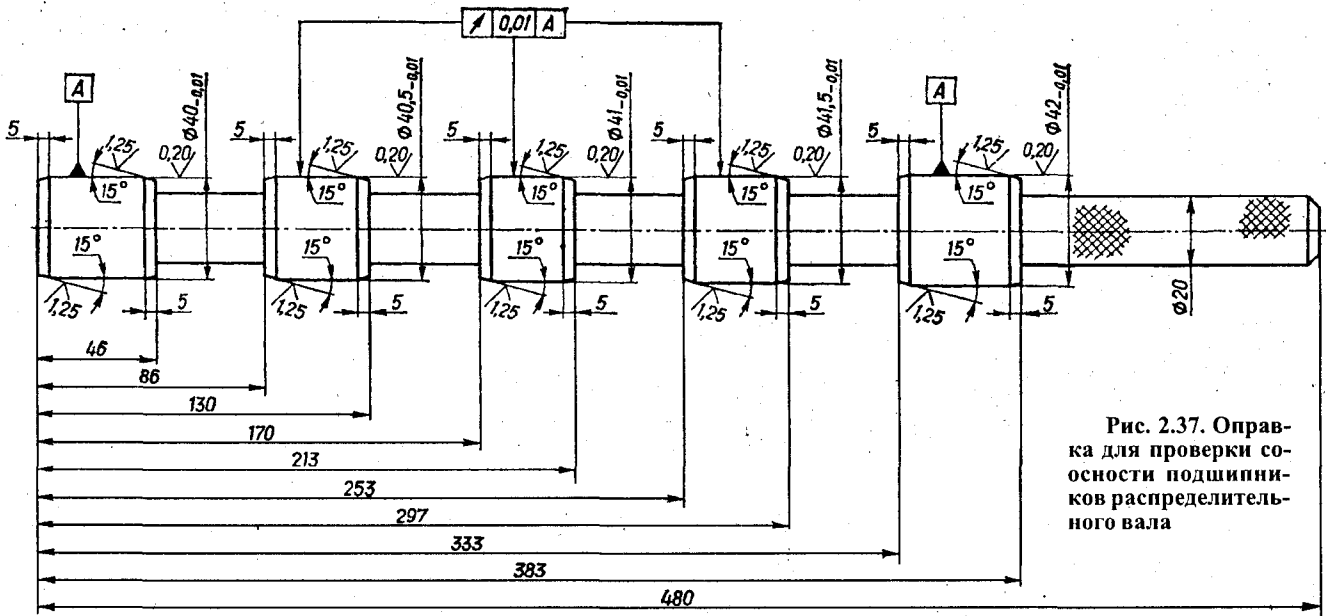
Оправка для проверки соосности подшипников распределительного вала
